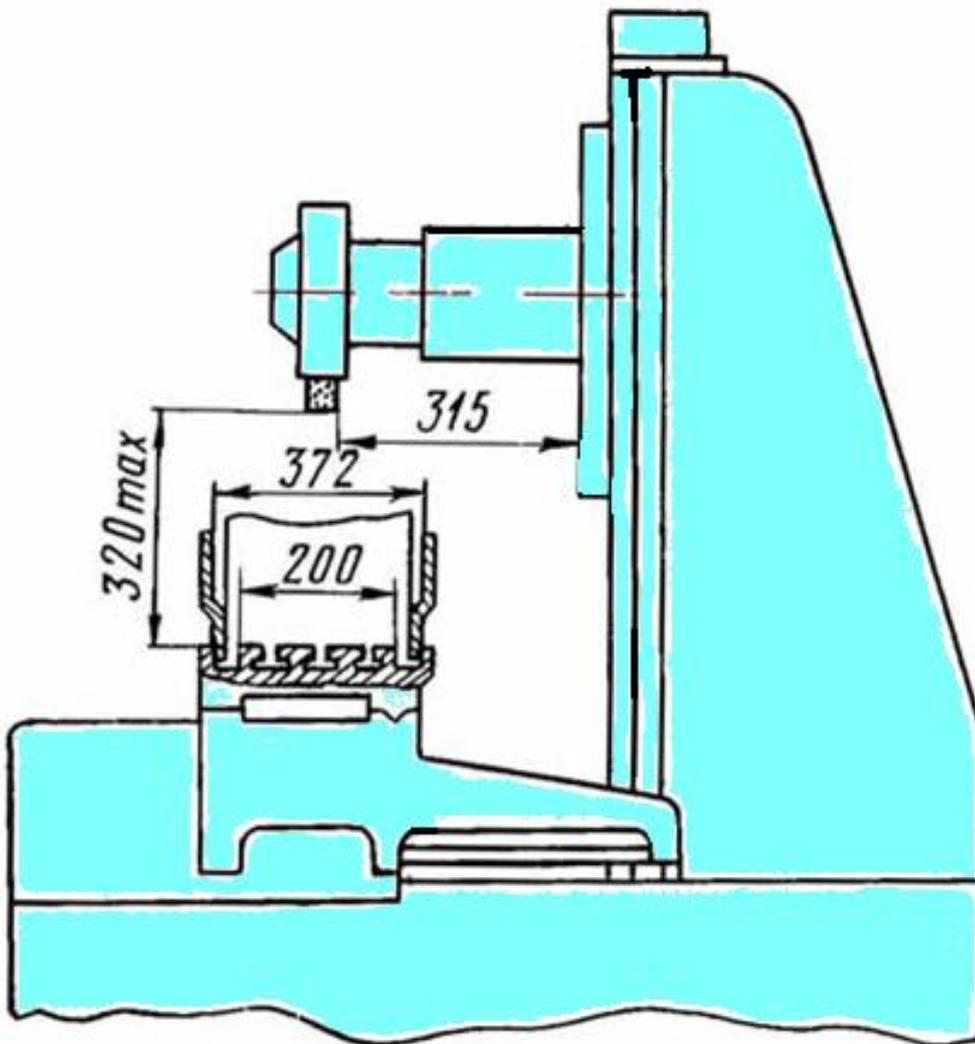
Основные размеры и посадочные места шлифовального круга станка 3Г71
